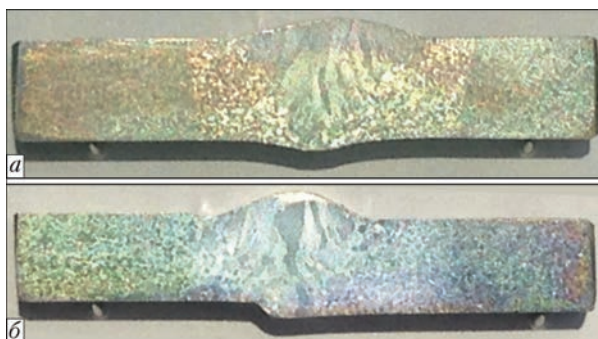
Вид сварных соединений сплава Ti–6,5Al–3Mo–2,5V–4Nb–1Cr–1Fe–2,5Zr, выполненных АДС: *а* — в разделку кромок; *б* — без разделки кромок с подачей присадочной проволоки марки ВТ1-00св
